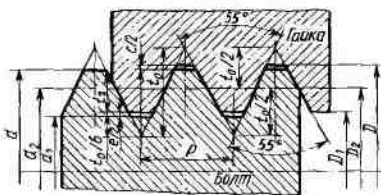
Профиль дюймовой резьбы: P — шаг резьбы, h_0 — теоретическая высота профиля, e — зазор по внутреннему диаметру, c — зазор по наружному диаметру
